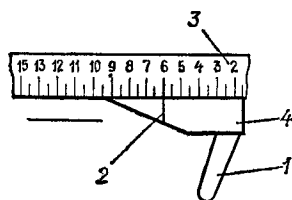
Измерение шагомером основного шага зубчатого колеса.
